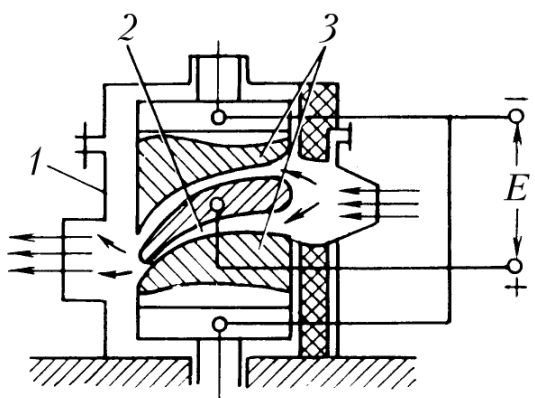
Схема електрохімічної обробки пера лопатки ГТД: 1 – манна камера; 2 – деталь; 3 – інструмент.
